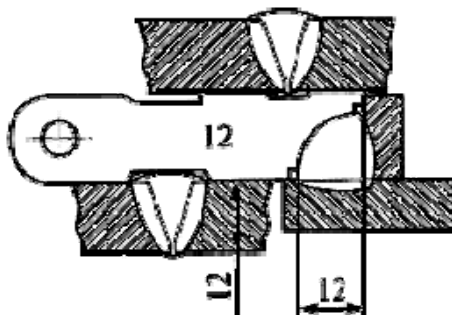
Специальный шаблон для контроля сварных швов
